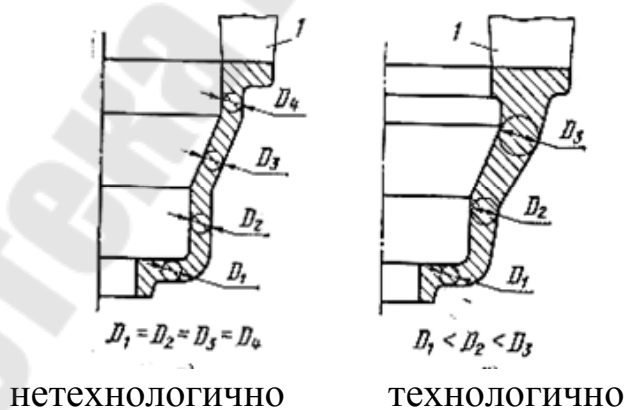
Рекомендуемое выполнение стенок для обеспечения более свободной усадки
